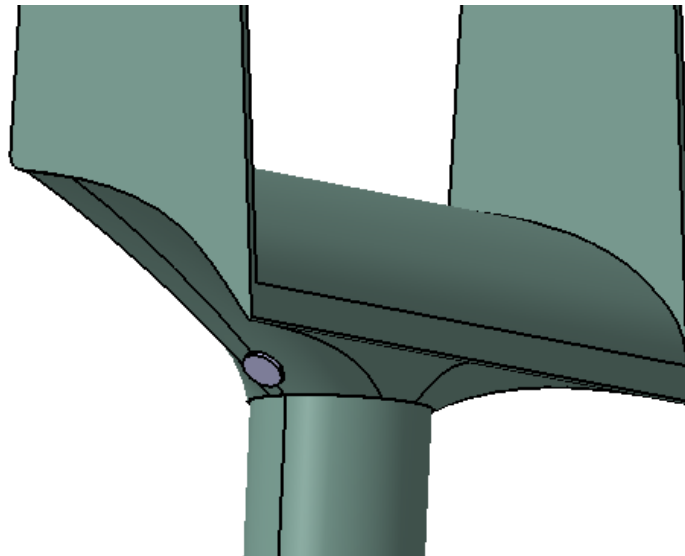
Pedal: Ensamblaje piezas 3 y 6
